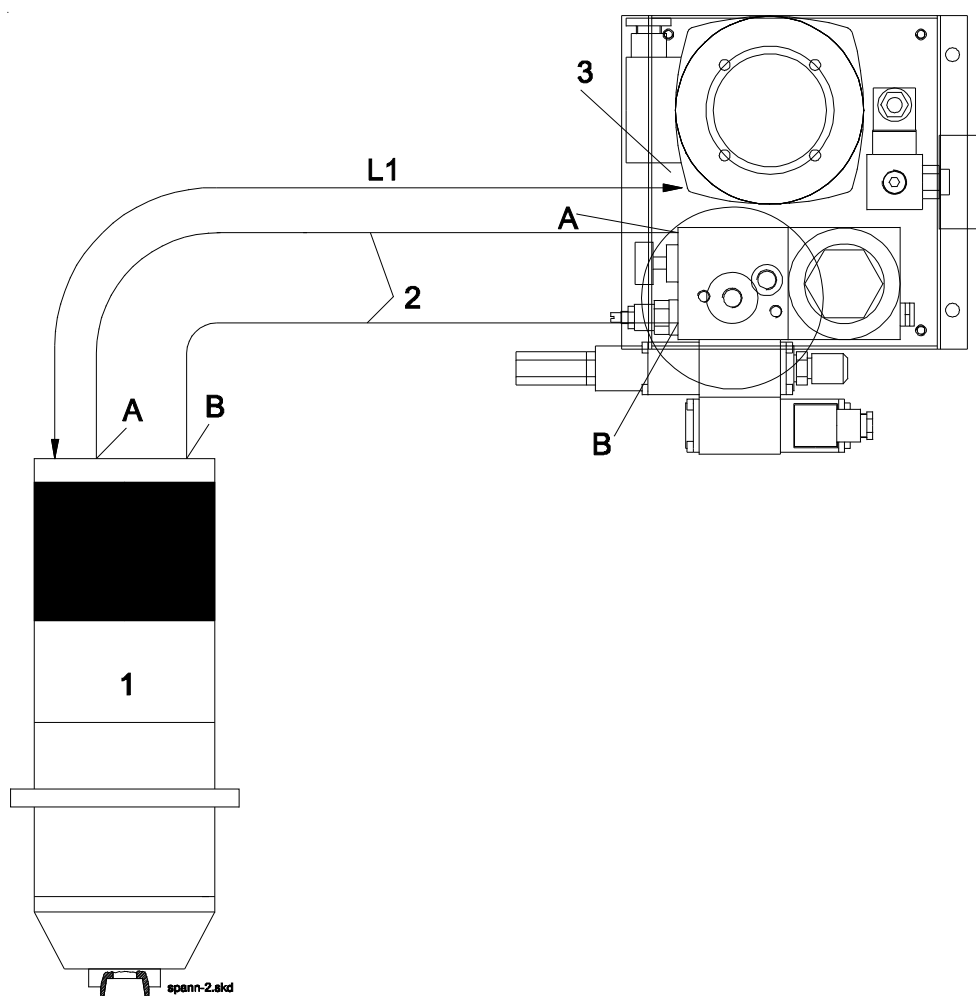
3: Panoramica di installazione per "Sistema idraulico di serraggio utensili"
